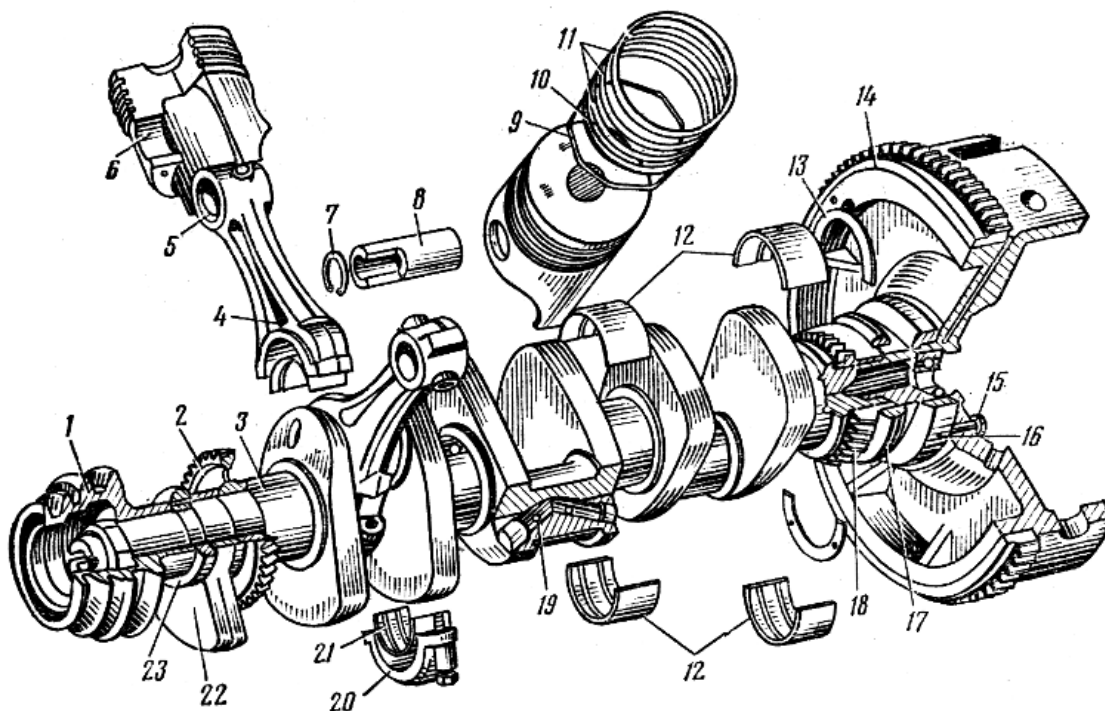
Кривошипно-шатунный механизм двигателя СМД-62:
